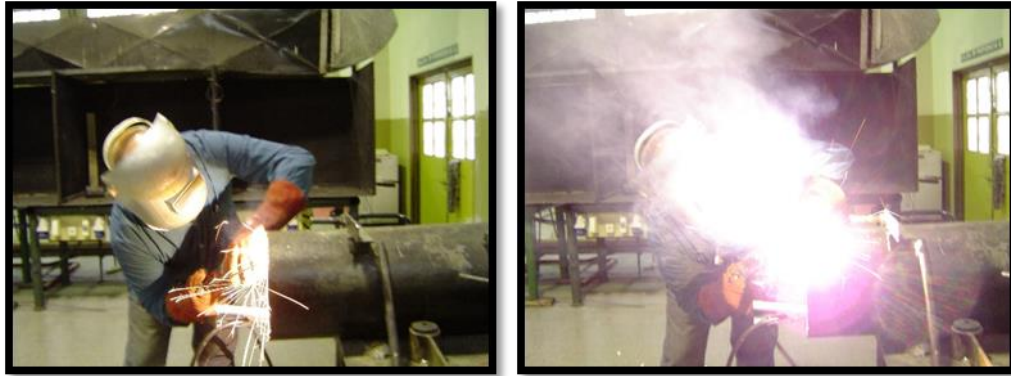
Operación De Soldadura, Taller Escuela Industrial - Fuente: Propia.
